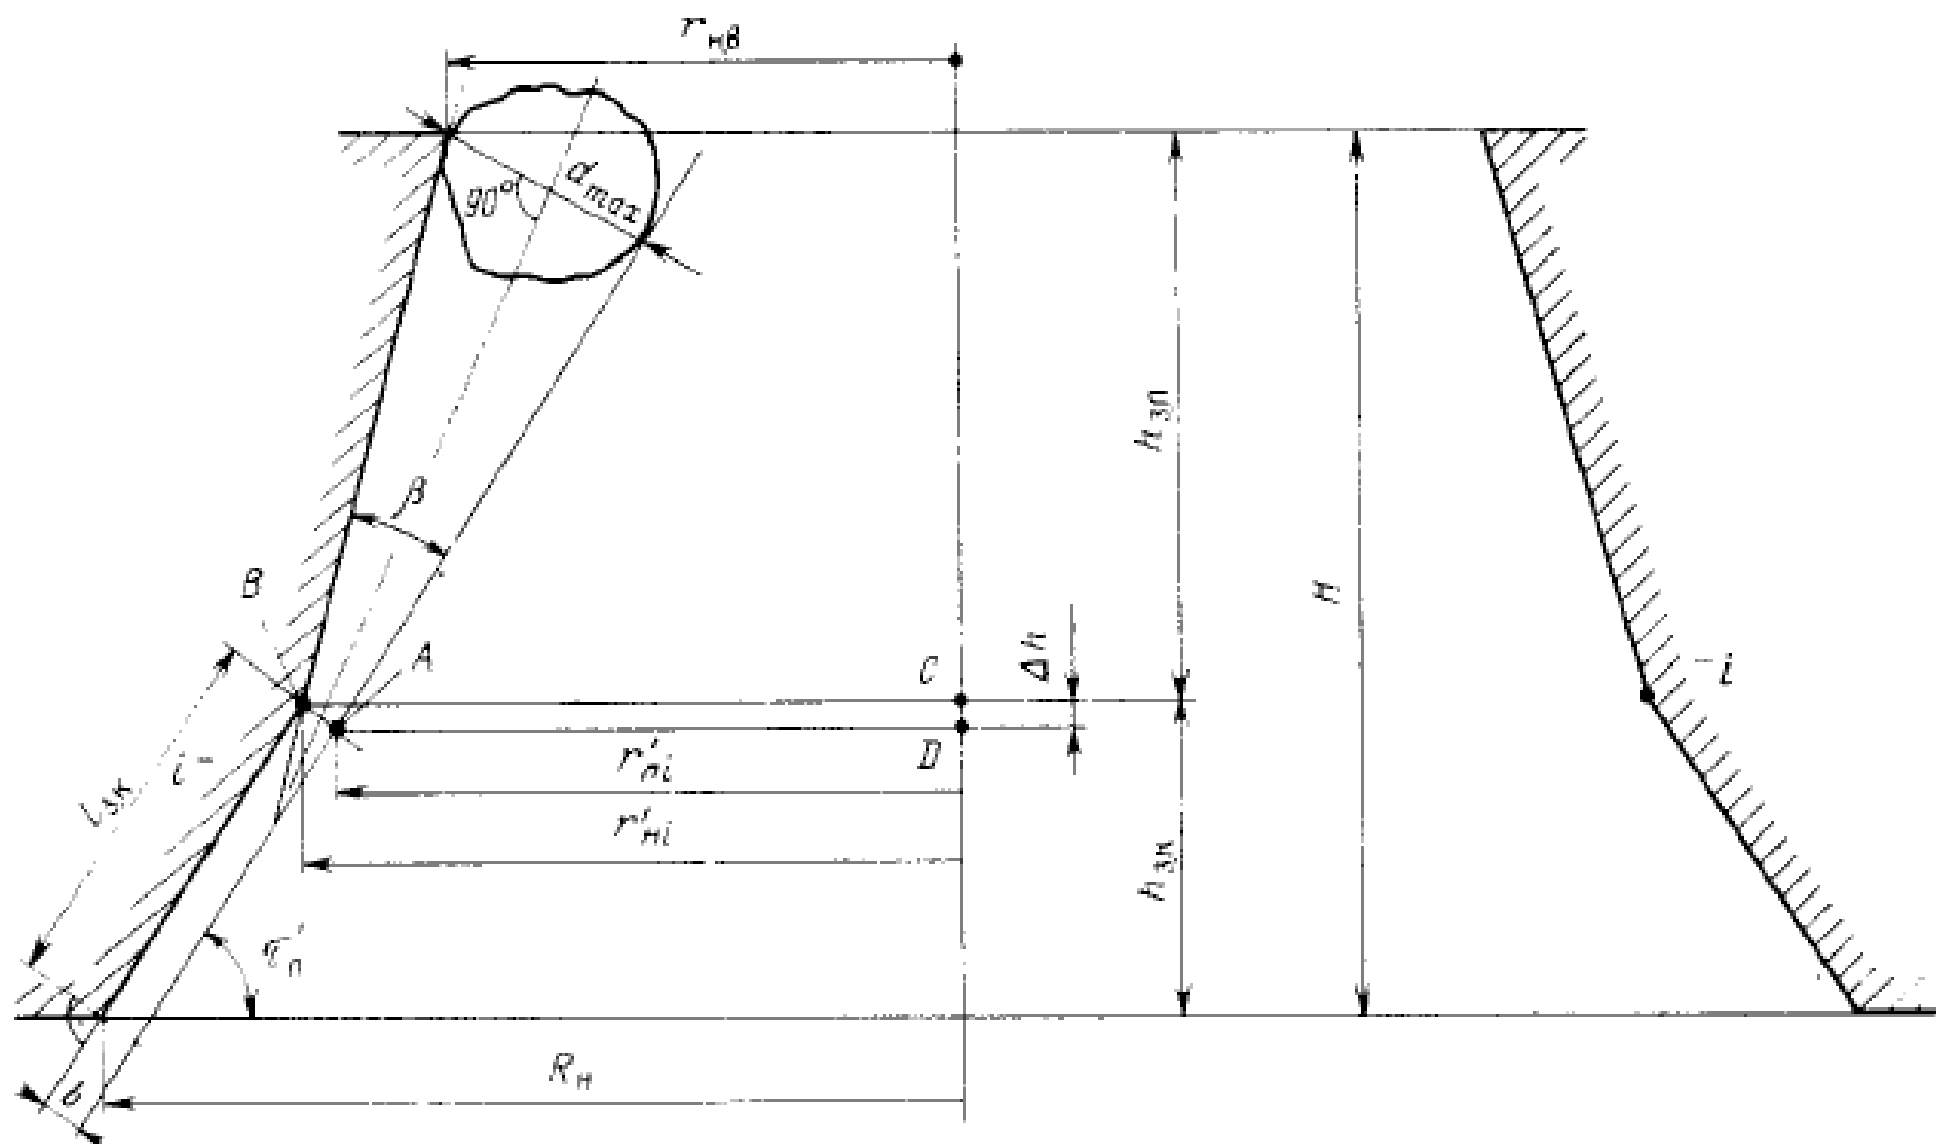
Схема побудови профілю камери дроблення дробарки типу КМД
